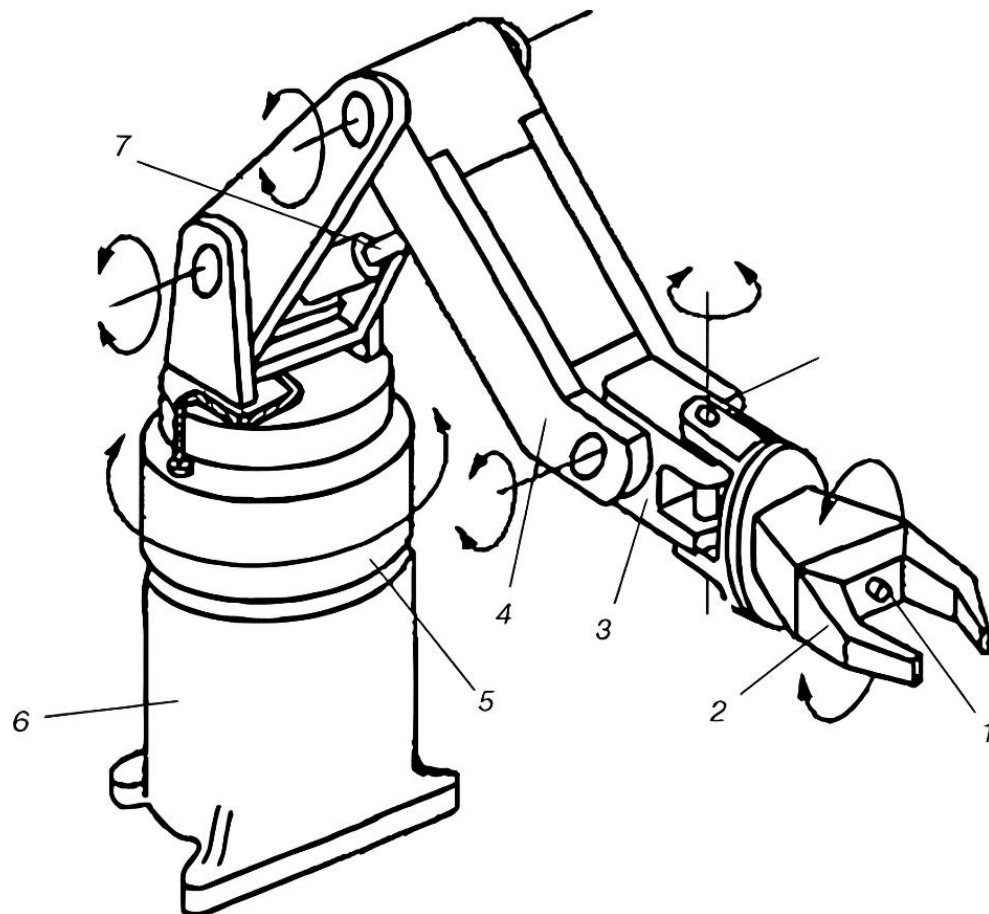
Схема конструкції промислового робота (1 – датчик зворотного зв’язку; 2 – захватний пристрій; 3 – пензель; 4 – рука маніпулятора; 5 – колона; 6 – несуча конструкція; 7 – привід руки)
